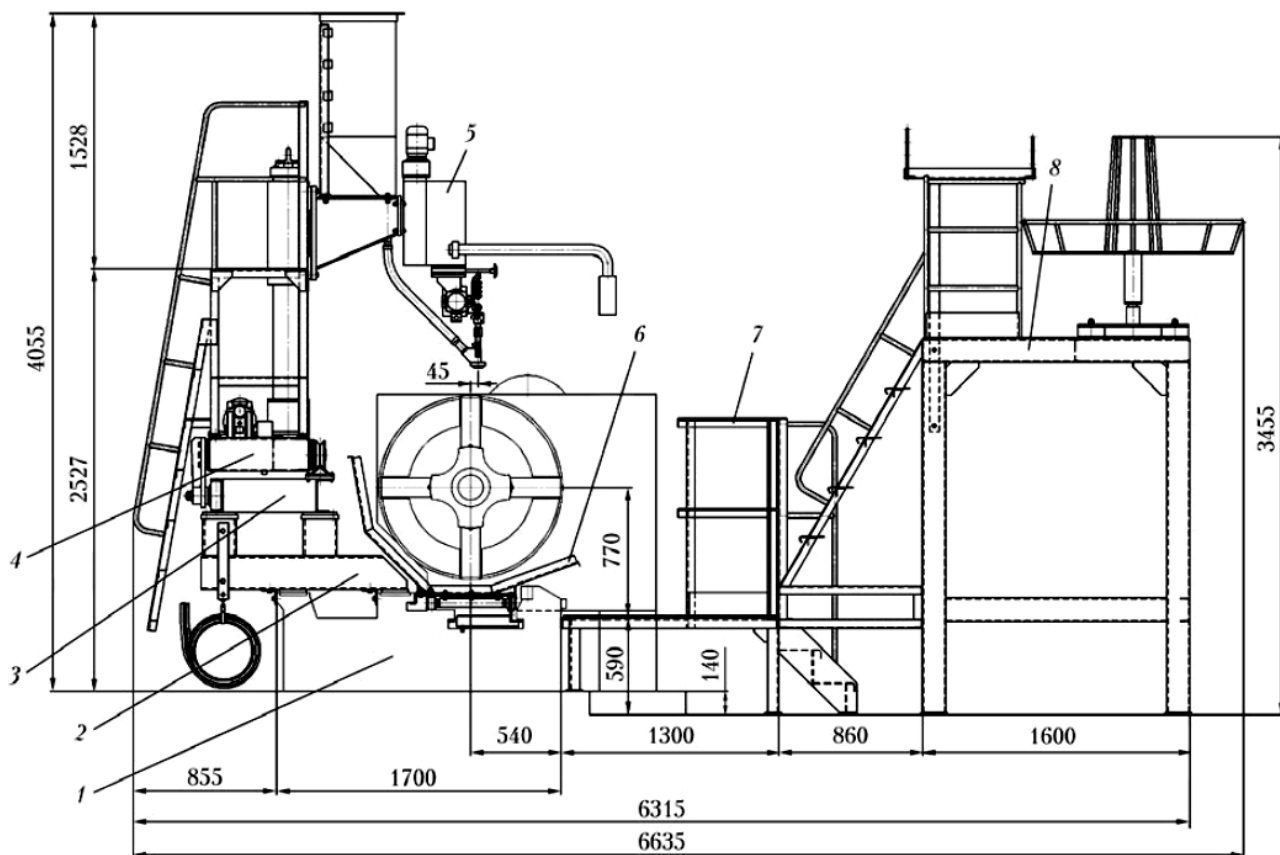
Схема установки установка РМ-12 для наплавлення прокатних валків заготівельних і сортових станів гарячої прокатки
